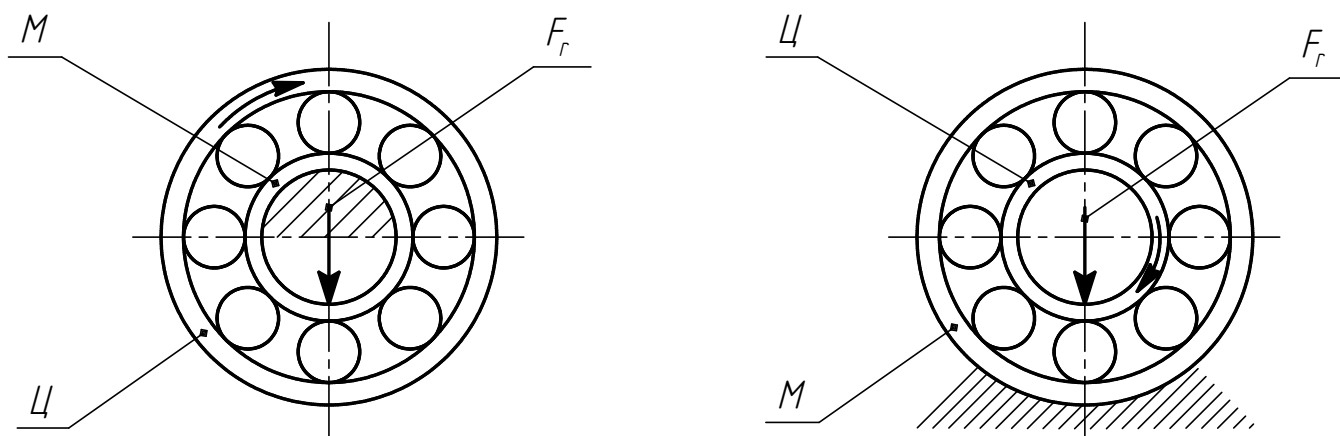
Схемы нагружения колец подшипников качения
